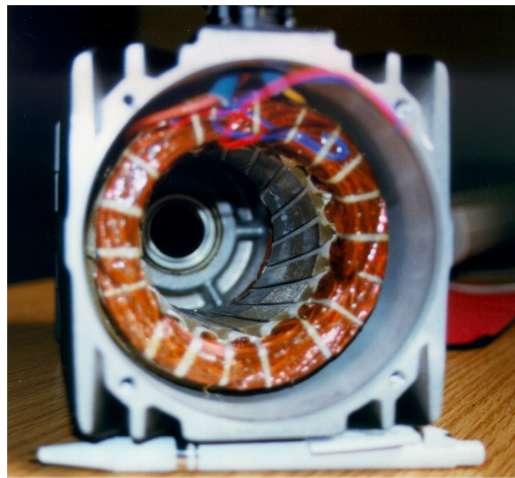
Bobinado en tambor de una máquina de flujo radial
